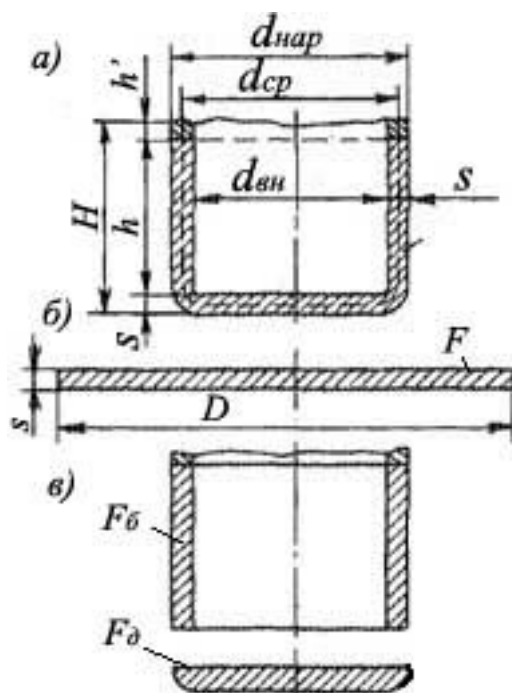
Схема разбивки цилиндра на элементы при расчете размеров заготовки: а – изделие; б – заготовка; в – элементы изделия
